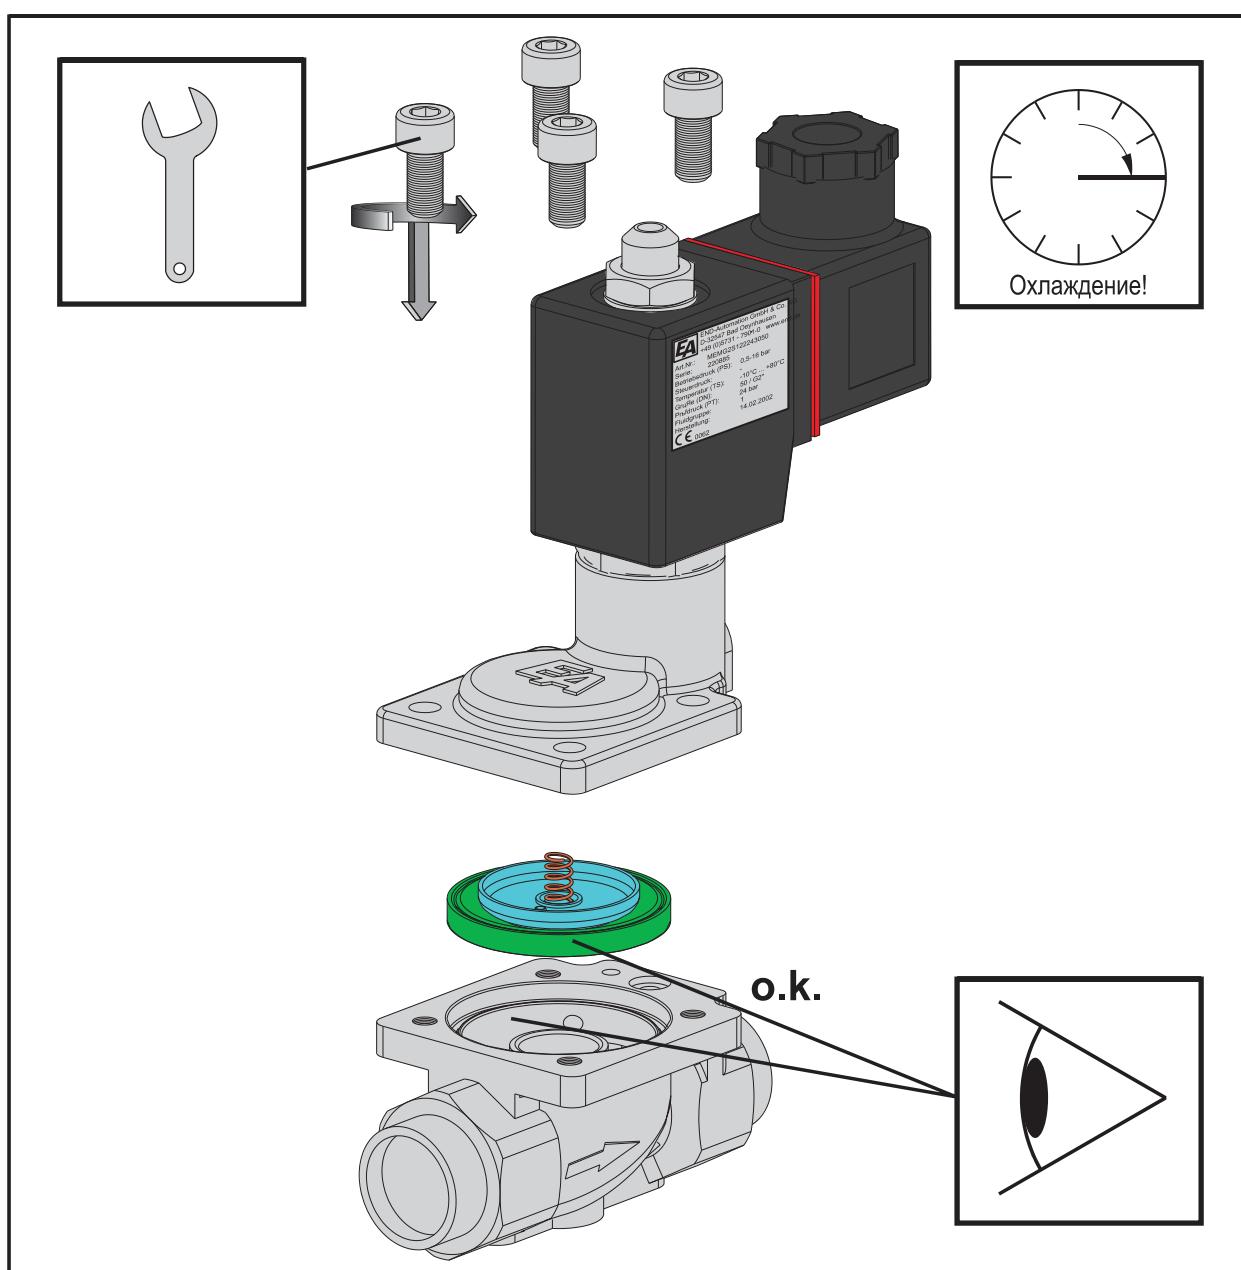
Монтаж/демонтаж – сварное соединение, установка верхней части клапана
